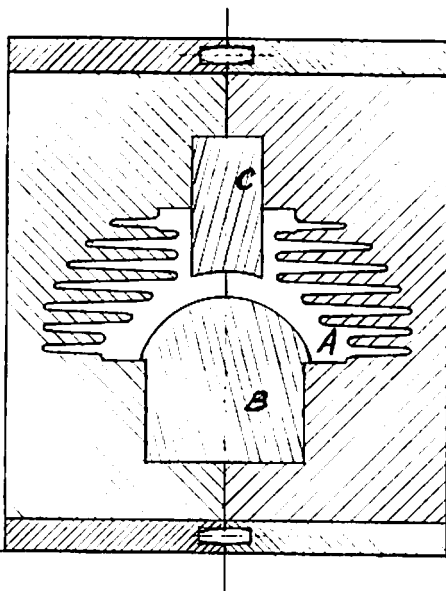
Gußform für einen Rippen-Zylinderkopf.
